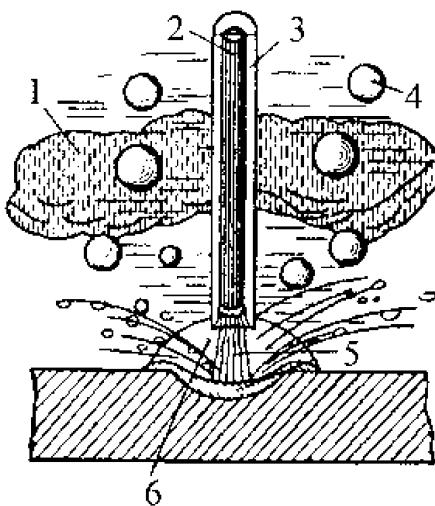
Схема горения сварочной дуги под водой
